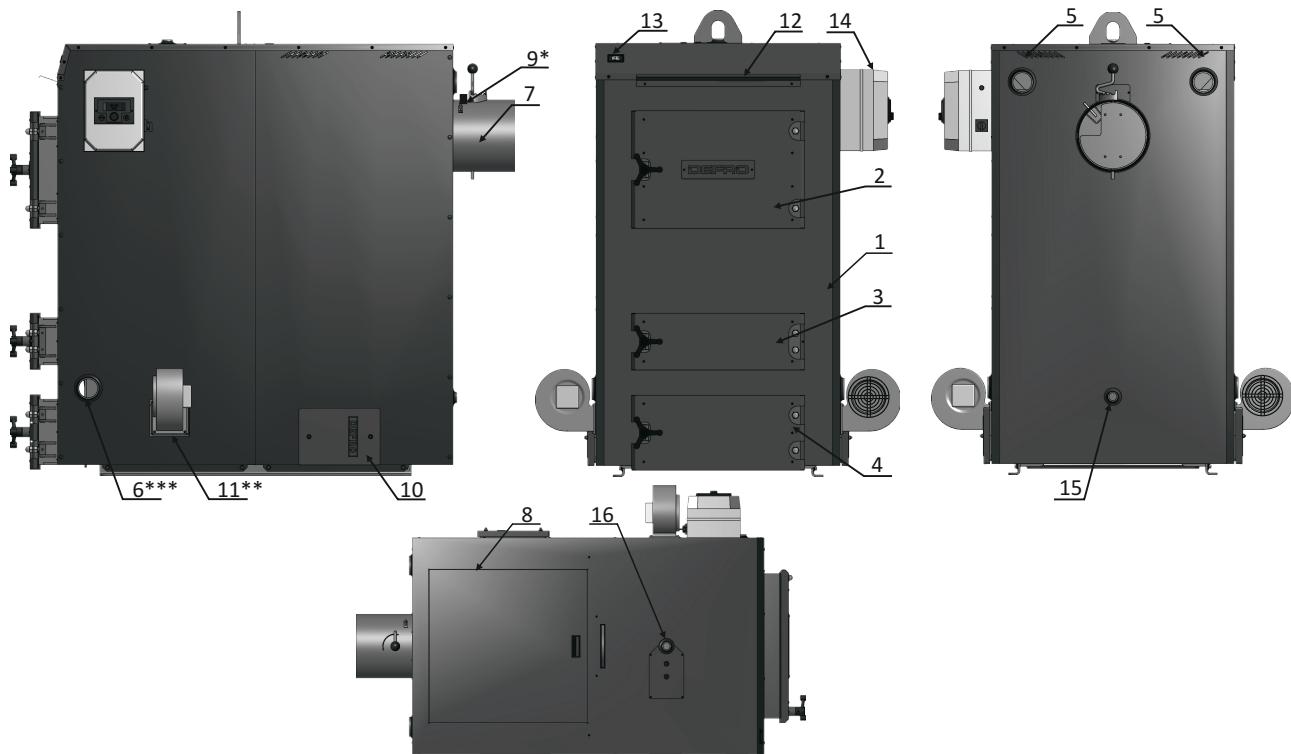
Основные части котла OPTIMA MAX PLUS: 1-стальной корпус с термоизоляцией; 2-засыпные дверцы; 3-топочные дверцы; 4-зольниковые дверцы; 5-питающий патрубок; 6-возвратный патрубок* (симметрично с двух сторон); 7-боров; 8-верхняя очистка; 9-заслонки (в котлах с мощностью 50-75кВт заслонки интегрирована с расширением борова); 10-боковая очистка; 11-вентилятор (в котлах с мощностью 50-75кВт только 1 шт.); 12-крышка; 13-аналоговый термометр; 14-регулятор; 15-спусковой патрубок; 16-воздухоотводящий патрубок
